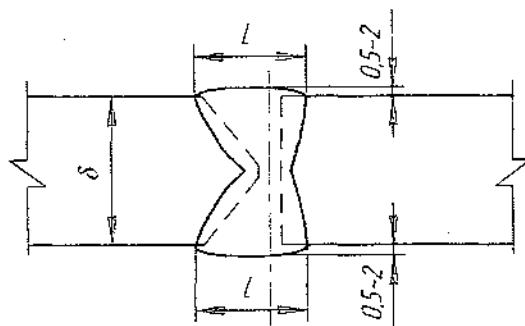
Схема сборки монтажных стыков толщиной 8–50 мм с К-образной разделкой кромок (С15) под автоматическую сварку в смеси защитных газов в вертикальном (наклонном) положении со свободным формированием шва (АППГ) для конструкций автодорожных и железнодорожных мостов любого типа исполнения
